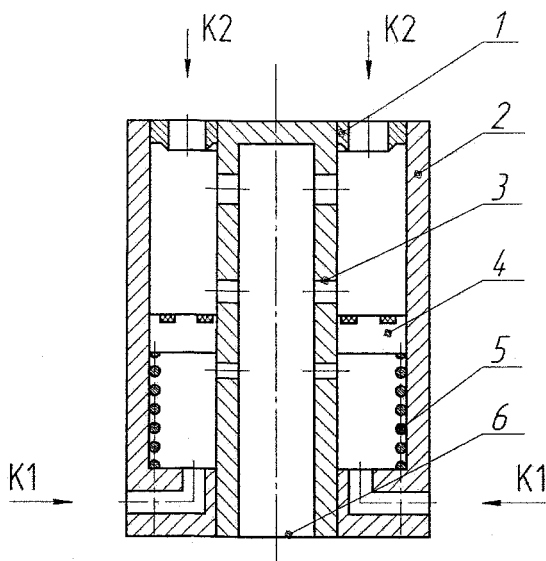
Двухкомпонентная многорежимная форсунка: 1 – седло; 2 – внешний корпус; 3 – внутренний корпус; 4 – поршень; 5 – пружина; 6 – сопло
